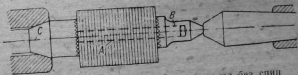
Оправка для фрезеровки колес с набором в промежутки между спицами.
